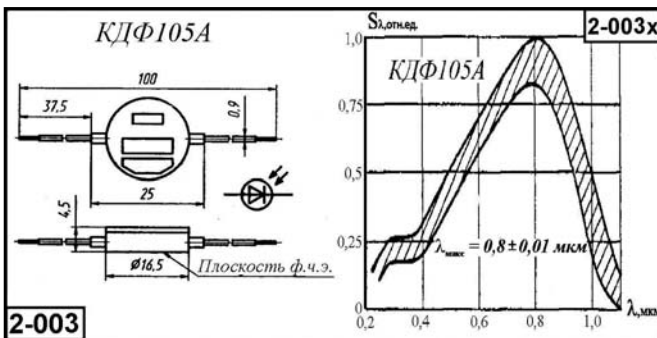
Внешний вид, габаритные размеры и ОСХ кремниевых фотодиодов
